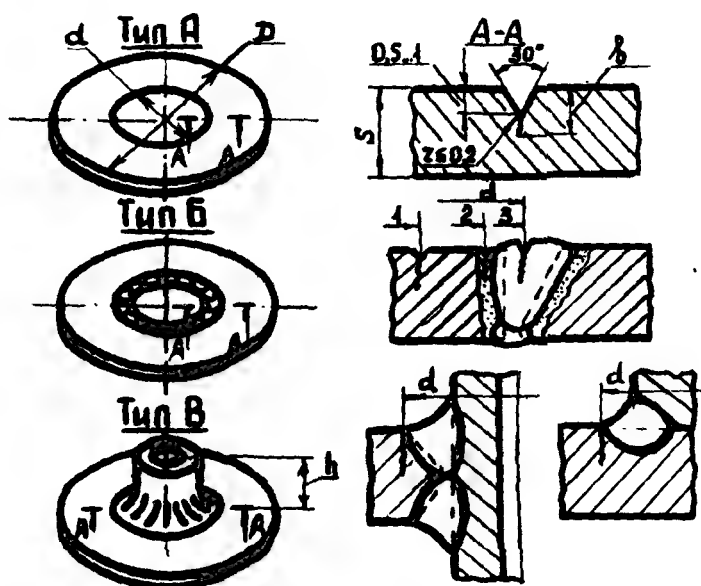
Типы дисковых образцов для оценки сопротивления коррозионному растрескиванию элементов сварных оболочковых конструкций
